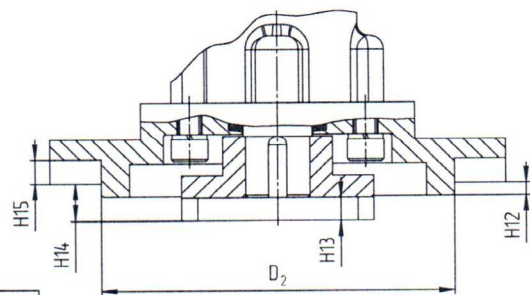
Присоединительные размеры входных вала и фланца редуктора РЗАМ-СХ-XXXX (остальное см. рис. 1 и 2).
